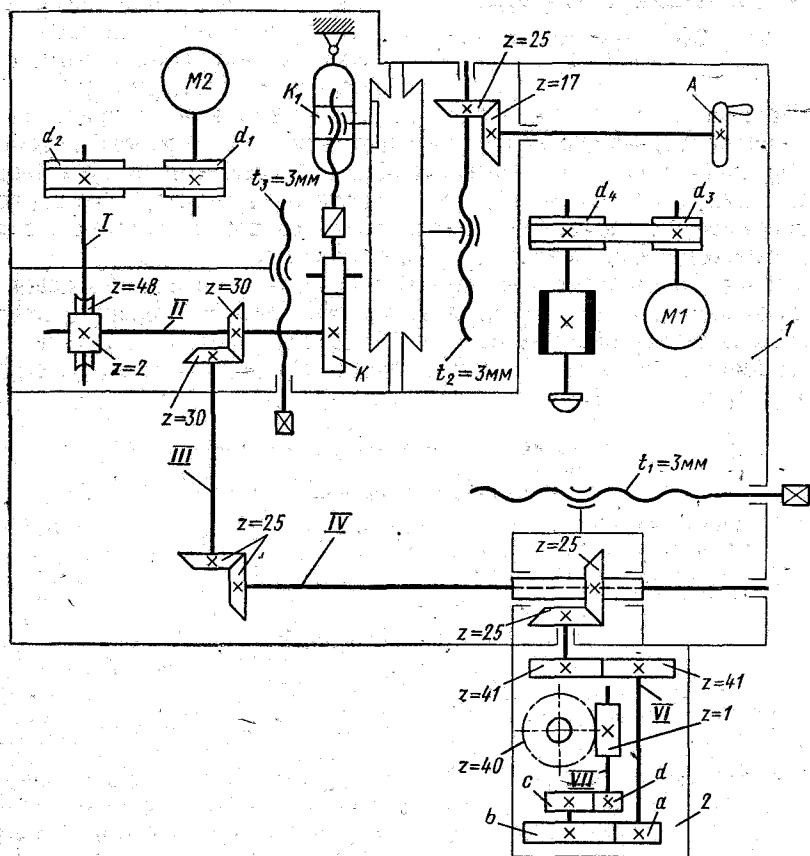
Кинематическая схема зубозакругляющего станка мод. 5582:
